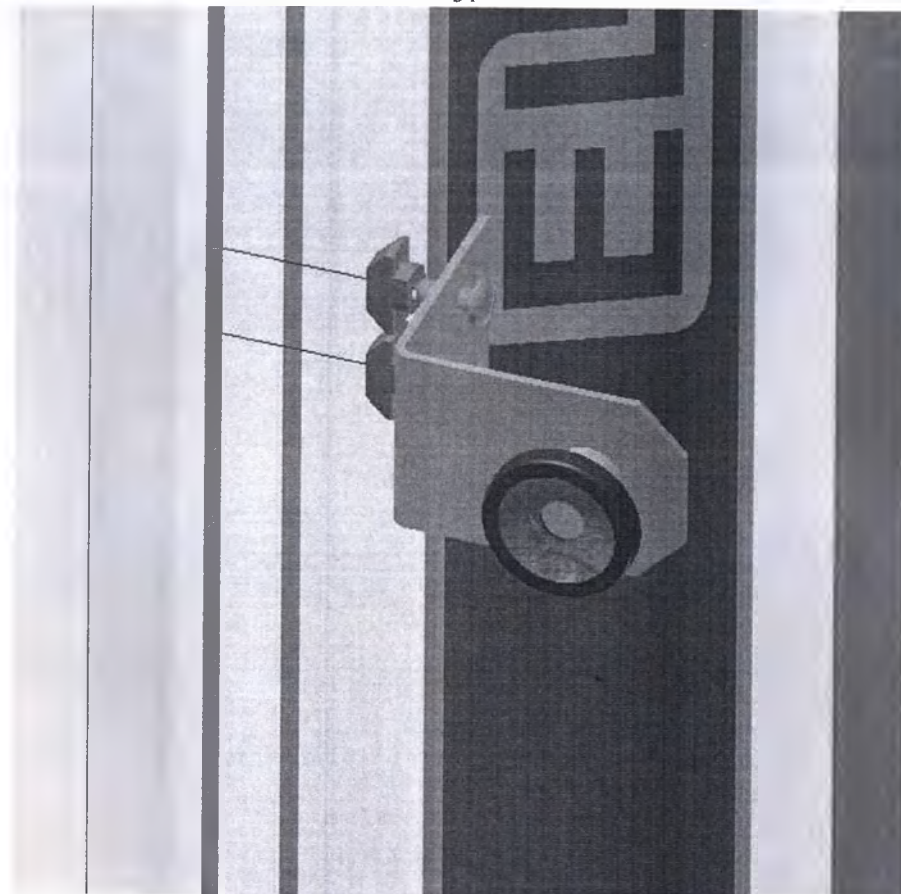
Установка держателя видеоголовки эндоскопической видеокамеры
